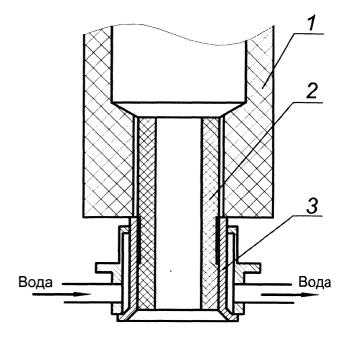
Тигель и кристаллизатор для литья полосы размером 20x5 мм: I — тигель; 2 — фильера; 3 — металлический водоохлаждаемый корпус
